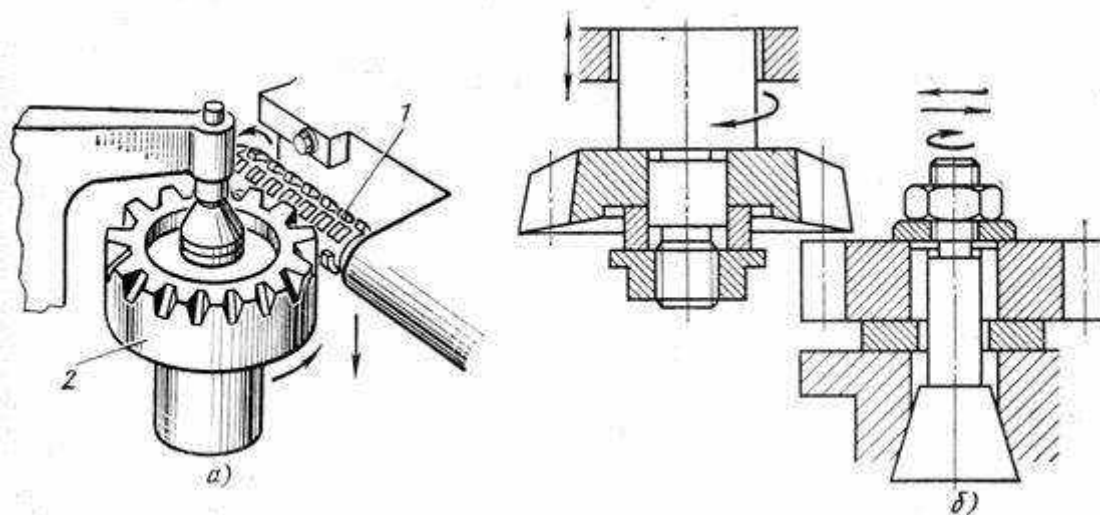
Схемы нарезания зубьев зубчатых колес методом обкатки:
